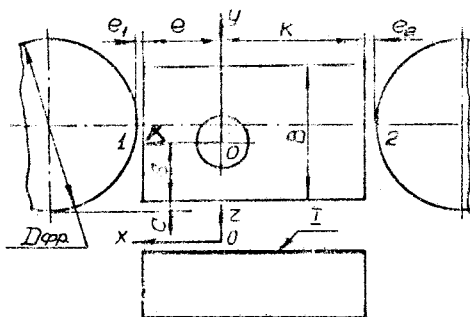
Схема резания при несимметричном фрезеровании торцевой фрезой плоскости I
